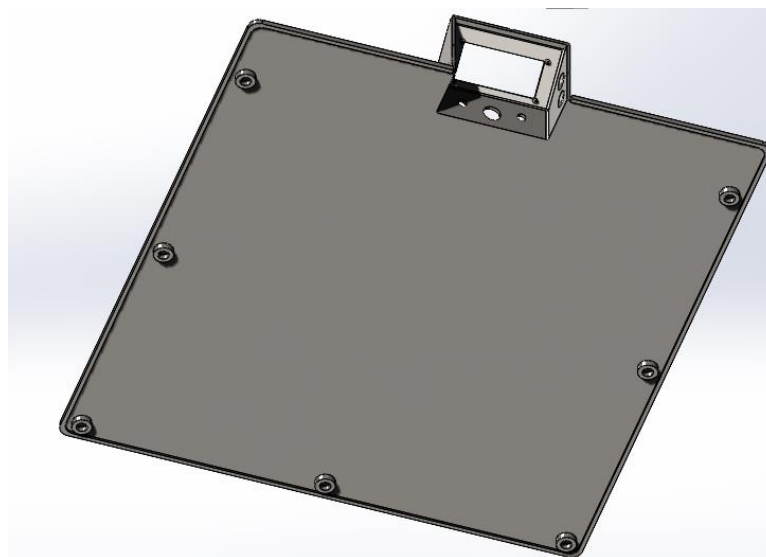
Деталь верхньої кришки корпусу, вид знизу
